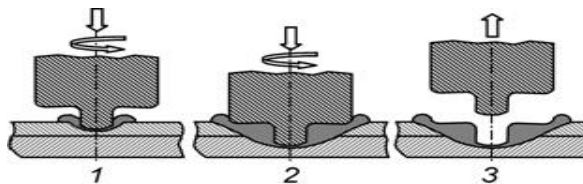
Стадии формирования сварного соединения при точечной сварке трением: 1 – стадия ввода рабочего стержня; 2 – стадия формирования сварной точки; 3 – стадия вывода рабочего стержня из зоны сварки
